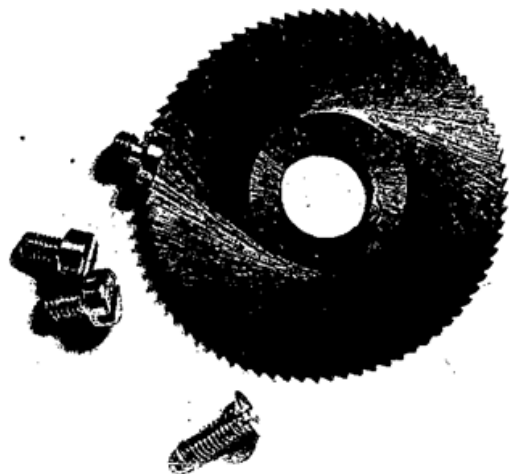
Внешний вид фрезы из нитрированной стали Р6М5 и крепежных болтов
